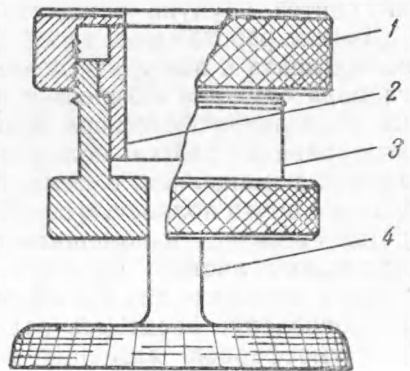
Схематическое изображение аппарата для получения испытуемых осадков; 1 — гайка, 2 — втулка, 3 — корпус, 4 — подвижный поршень
